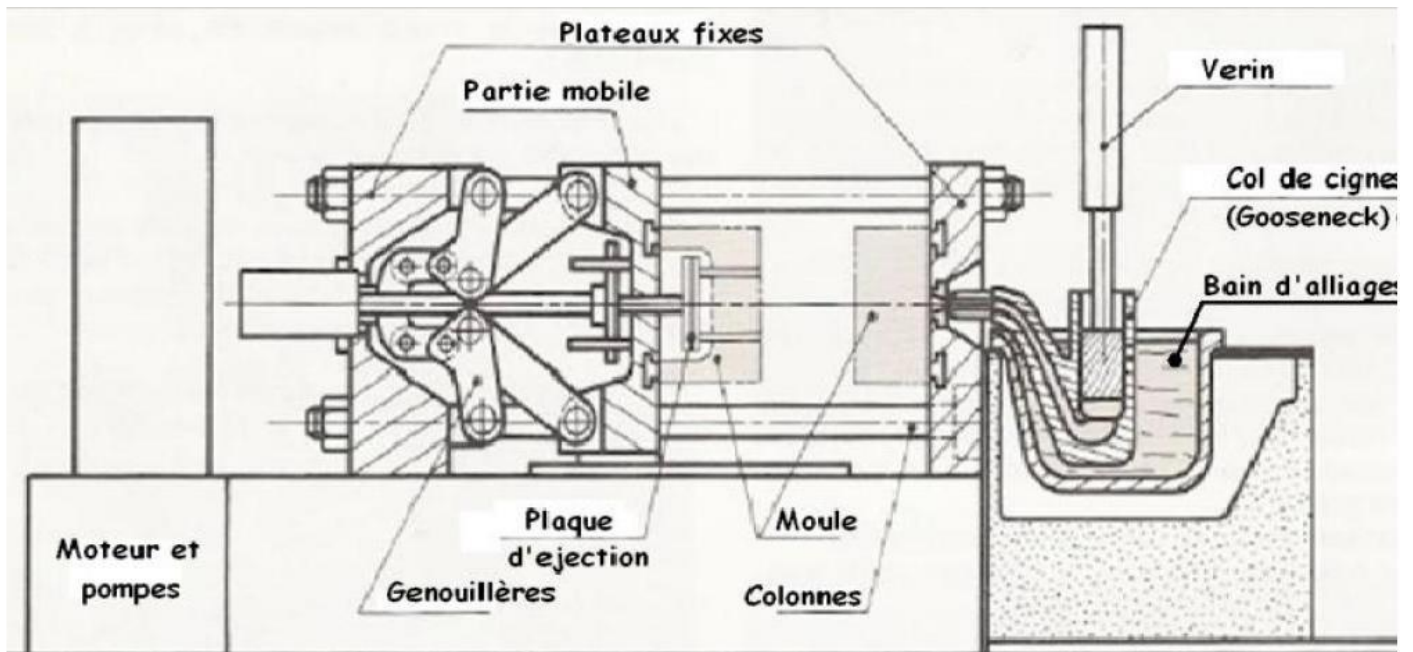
Principe du moulage en coquille sous pression de machines à chambre chaude
